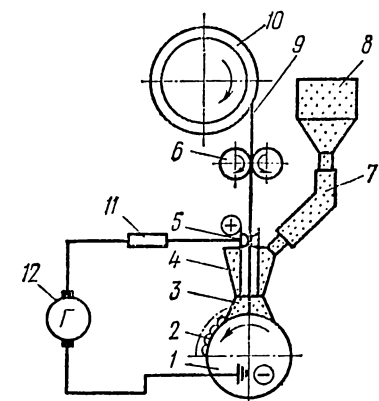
Схема установки для автоматической наплавки под слоем флюса:
